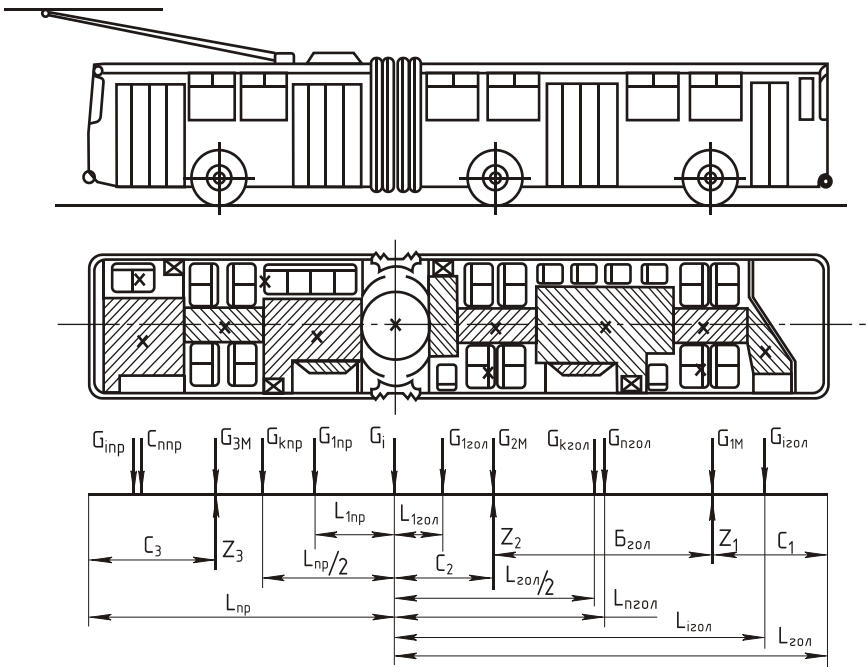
Планировка салона и расчетная схема нагрузок сочлененного троллейбуса
